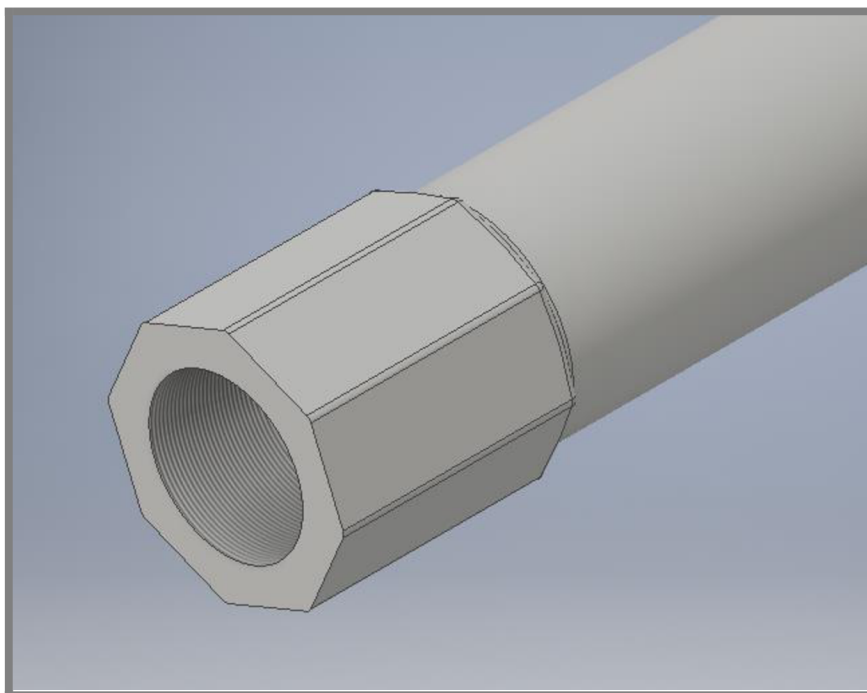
Drážka pro vedení držáku pomocného dalekohledu
